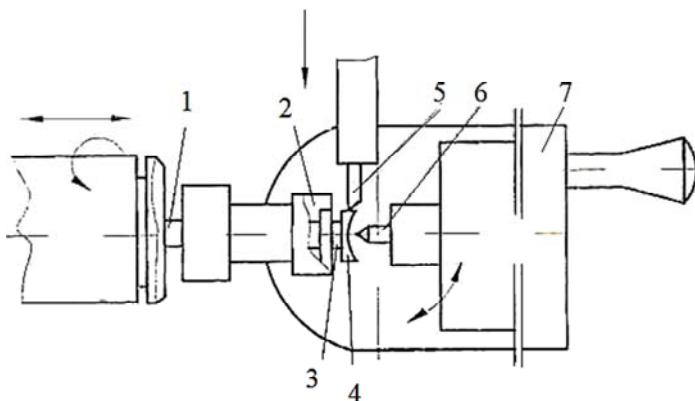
Схема точения вогнутой поверхности линзы на станке КП61:
